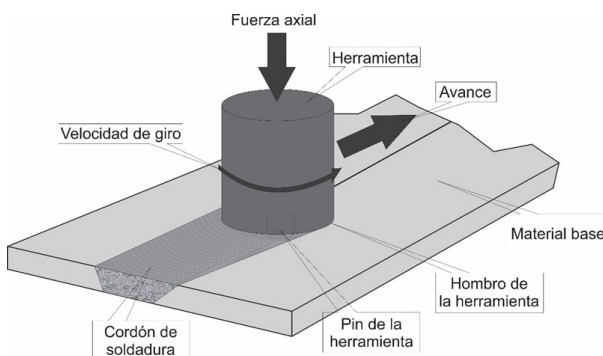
Esquema de funcionamiento del proceso de soldadura por FSW
